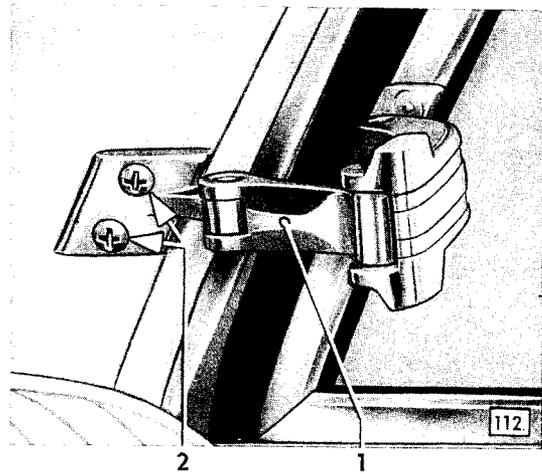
Ziehverschuß am Dachrahmen befestigt
